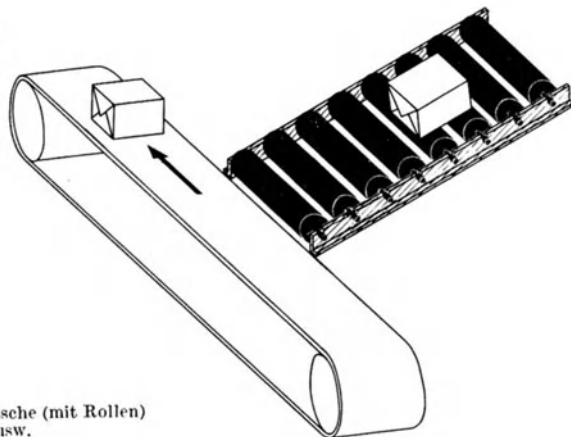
Geradlinige Rutsche (mit Rollen) für Pakete usw.
